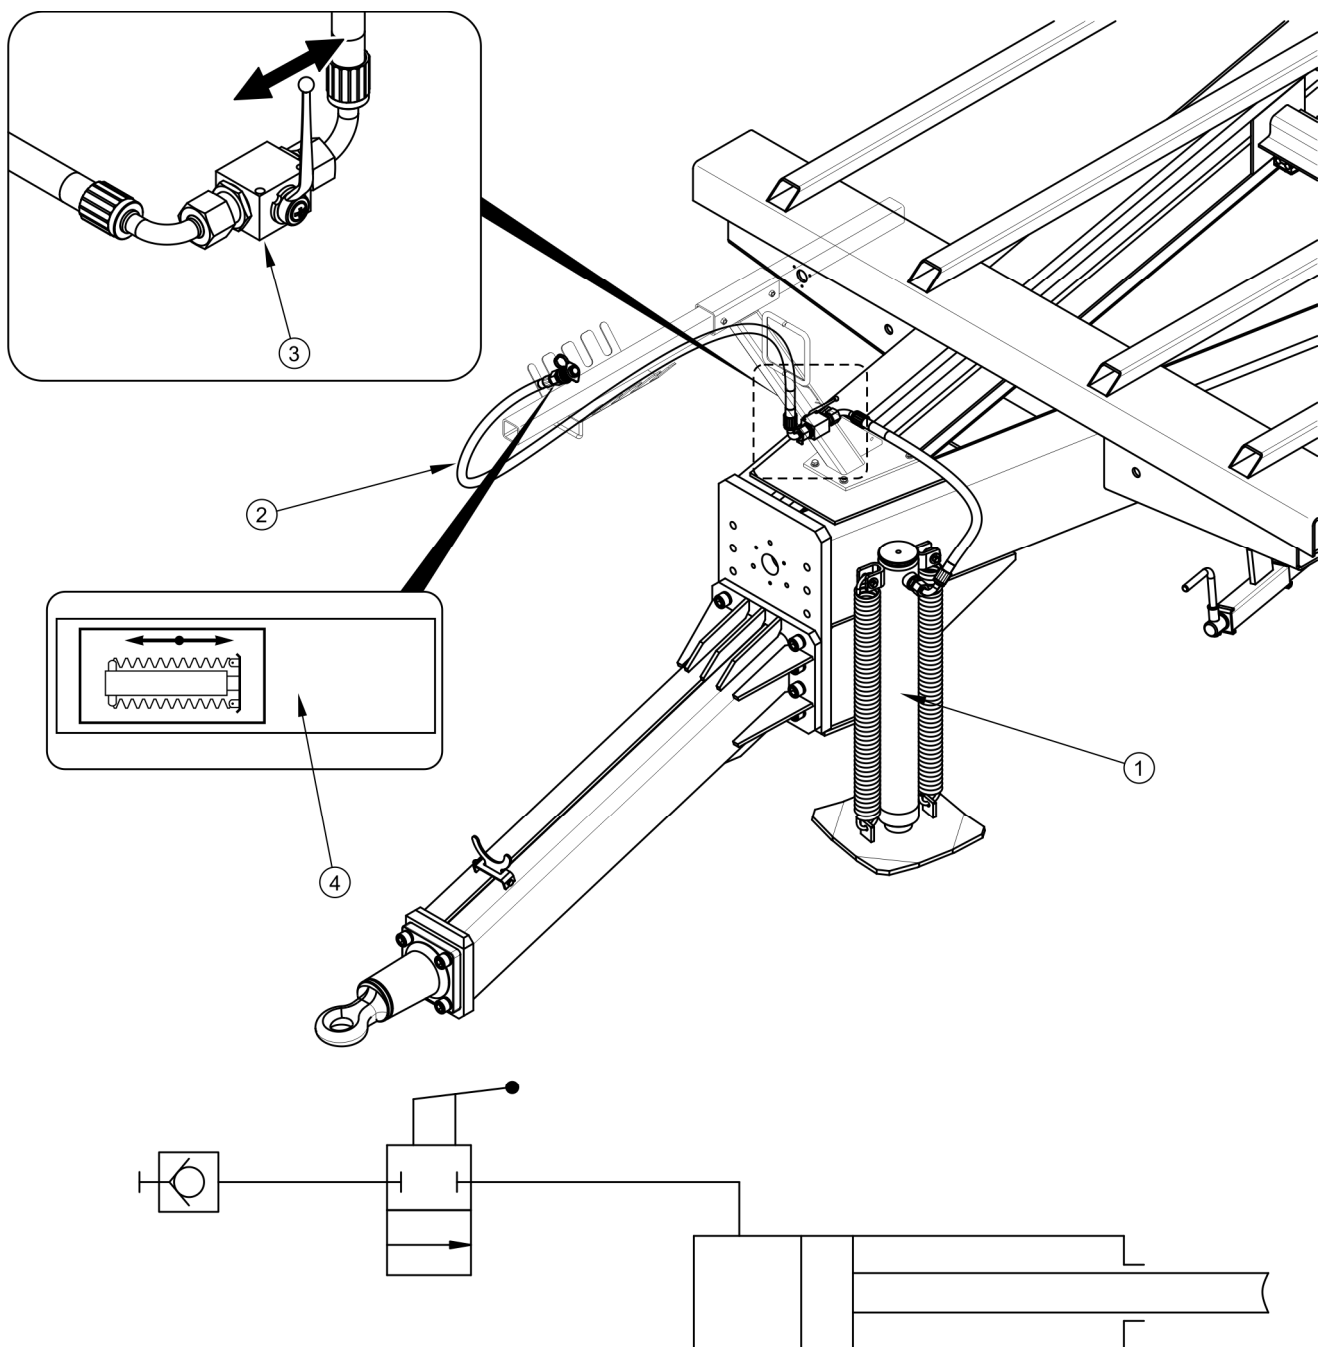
Konstrukce a schéma hydraulické instalace podávacího mechanismu
